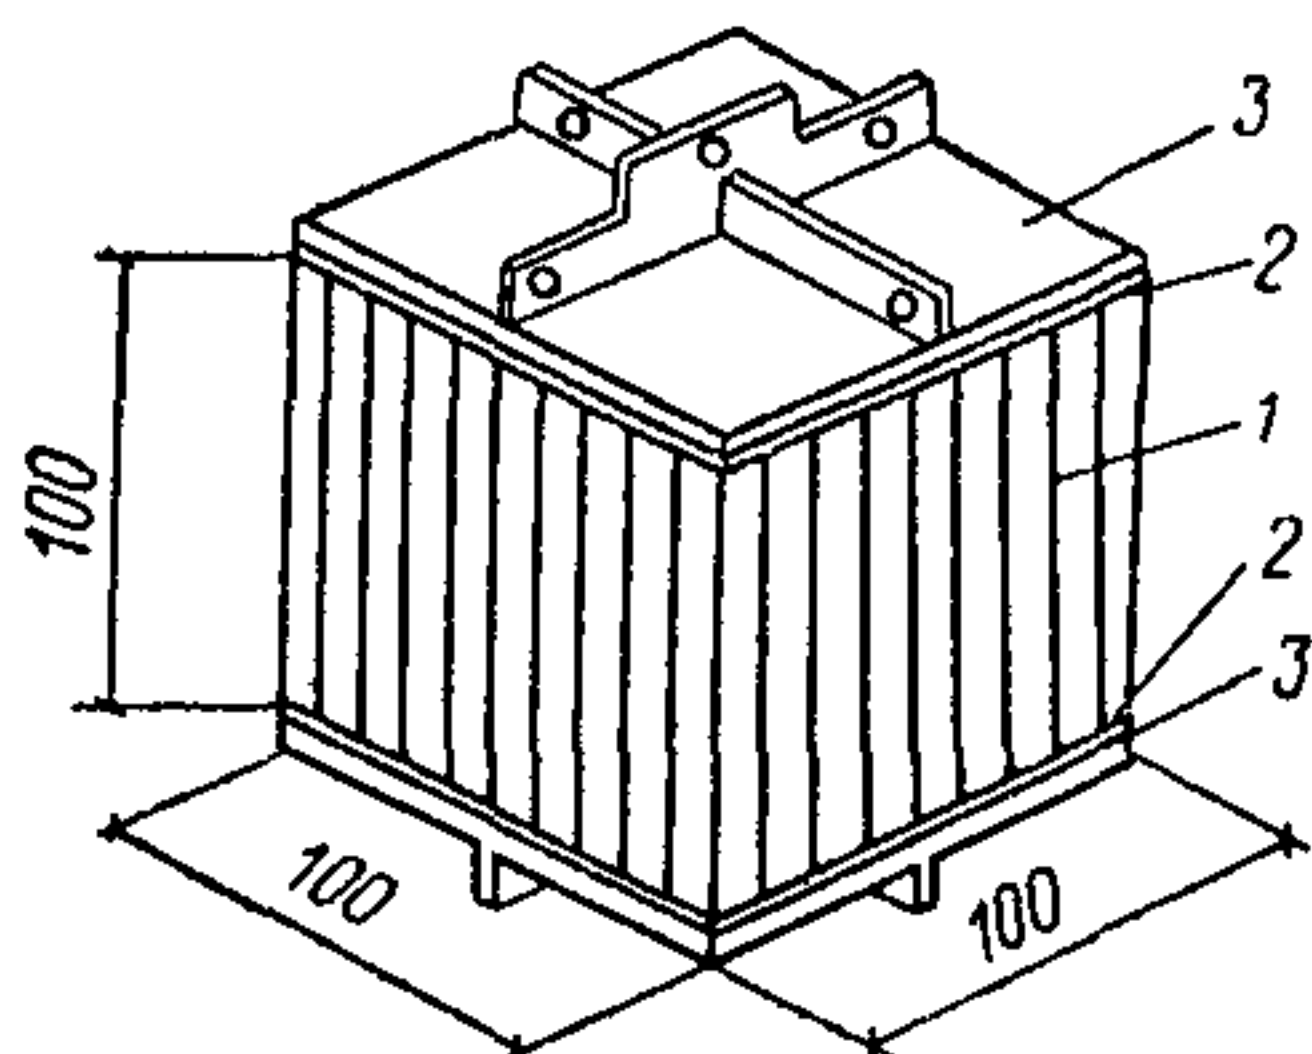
Форма и размеры составного образца для испытания прочности при растяжении сотопласта
